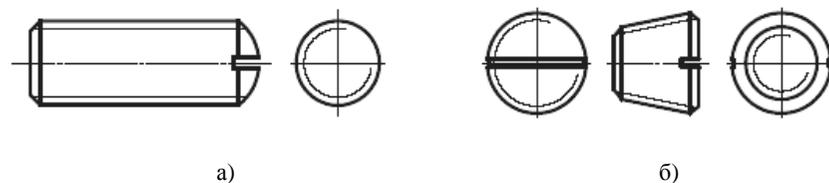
Изображение наружной цилиндрической (а) и конической (б) резьбы
